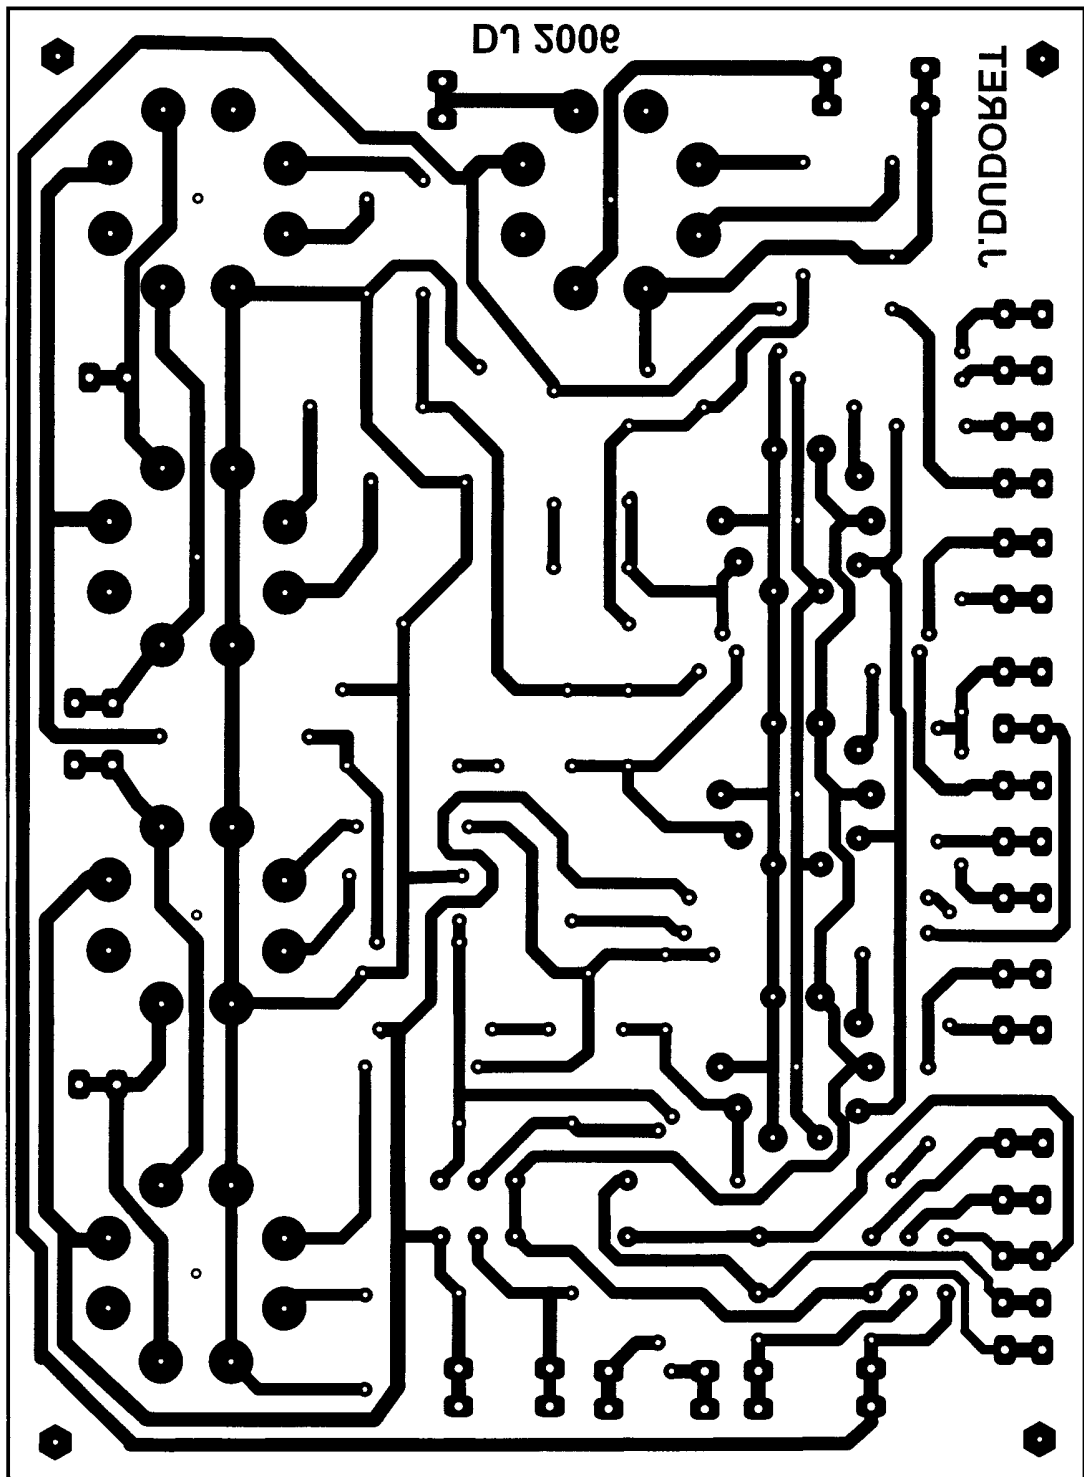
PCB platine à tubes (Dimensions 146 x 198 mm)
